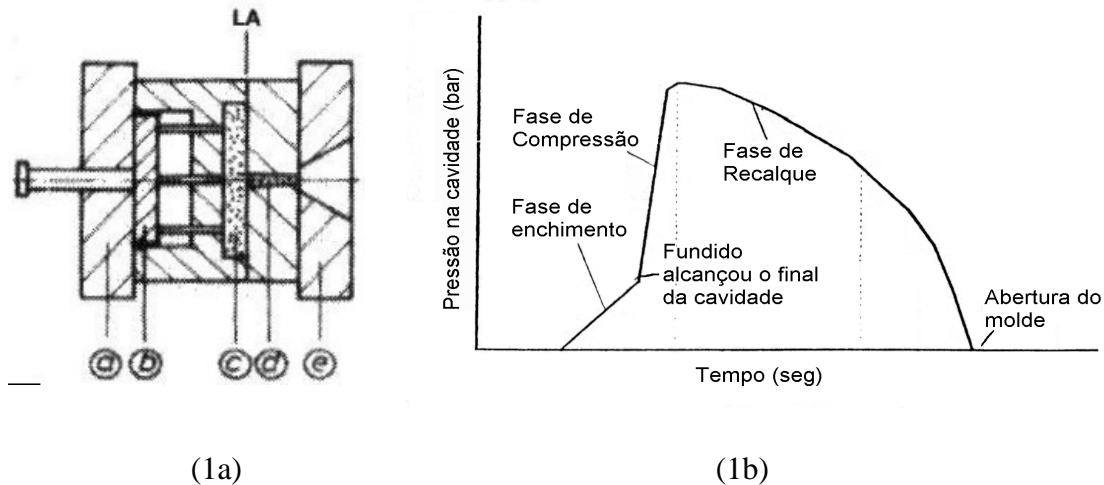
Molde para injeção: (1a) Partes principais: a) placa móvel; b) sistema de extração; c) cavidade; d) canal de alimentação; e) placa fixa; LA: linha de abertura do molde.
